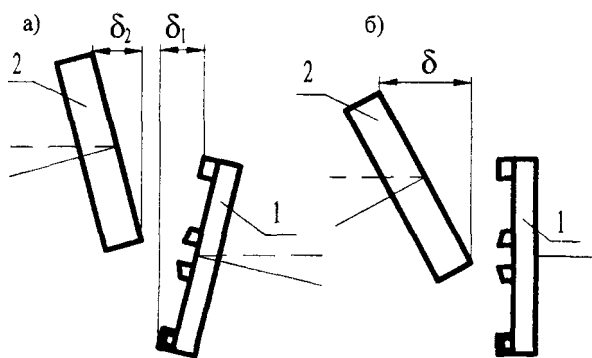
Схема образования погрешности при неточном относительном положении инструмента и заготовки
